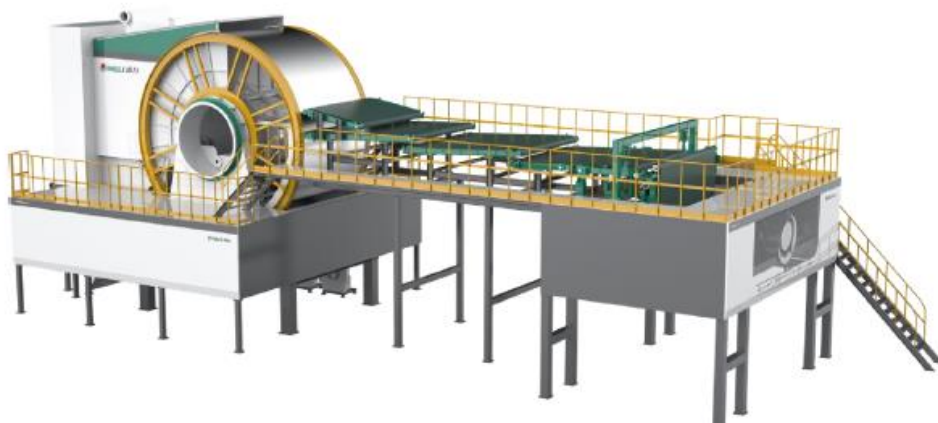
Внешний вид машины для сбора ваты, конвейера для сбора нитей и маятника
